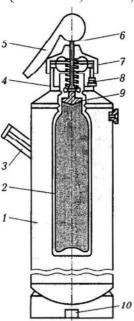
Химический переносной огнетушитель ОХП-10: 1 — корпус; 2 — кислотный стакан; 3 — ручка; 4 — горловина; 5 — рукоятка; 6 — шток; 7 — крышка горловины с запорным устройством; 8 — спрыск; 9 — резиновый клапан; 10 — пробка
